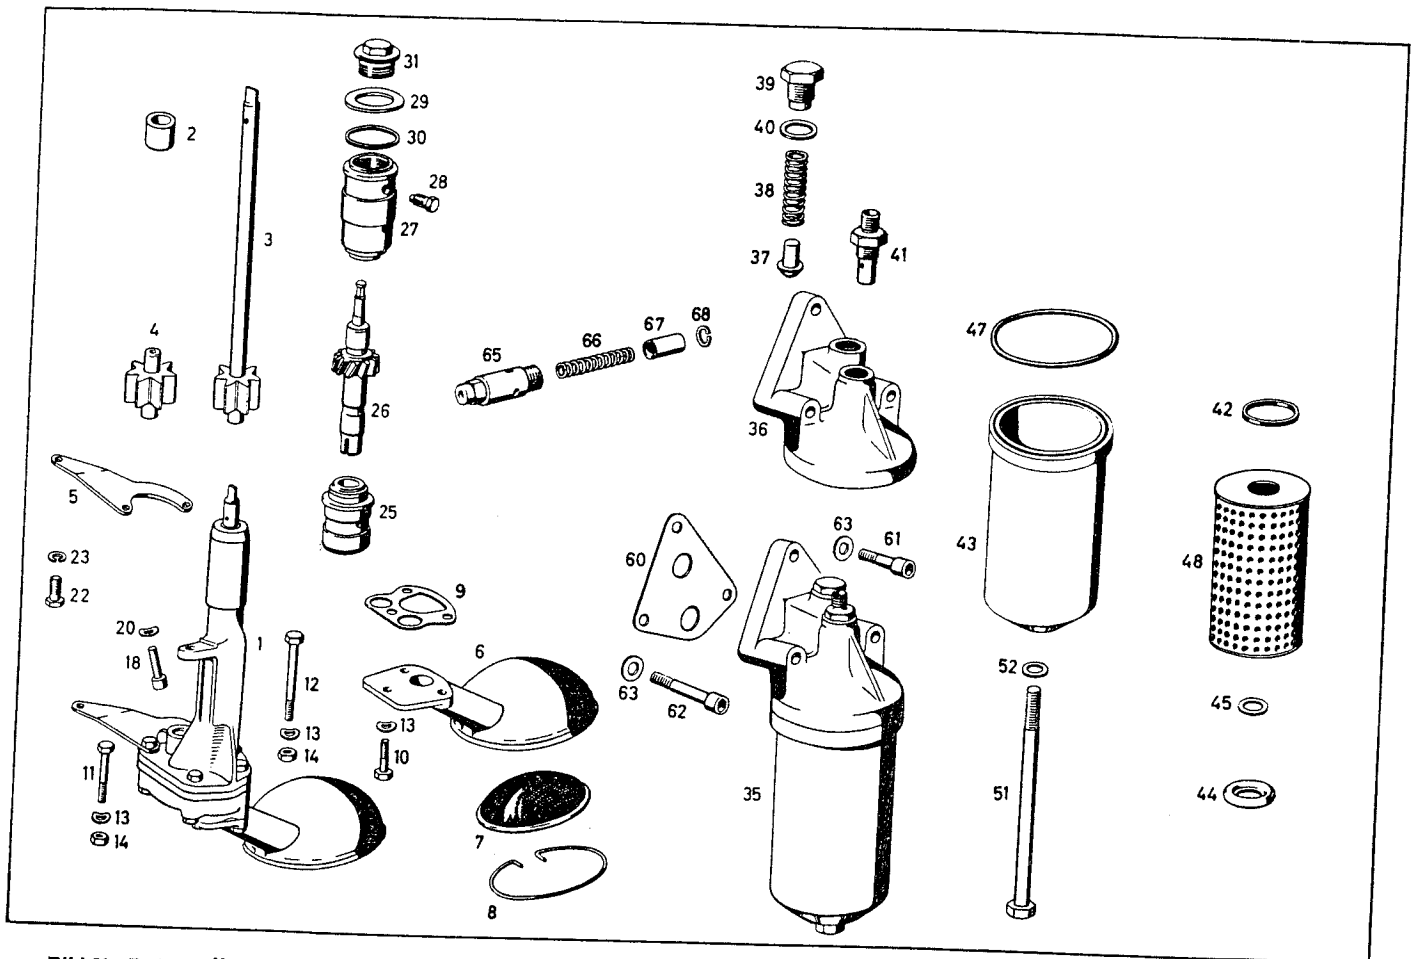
Zerlegte Ölpumpe, mit Filter (OM 621)
